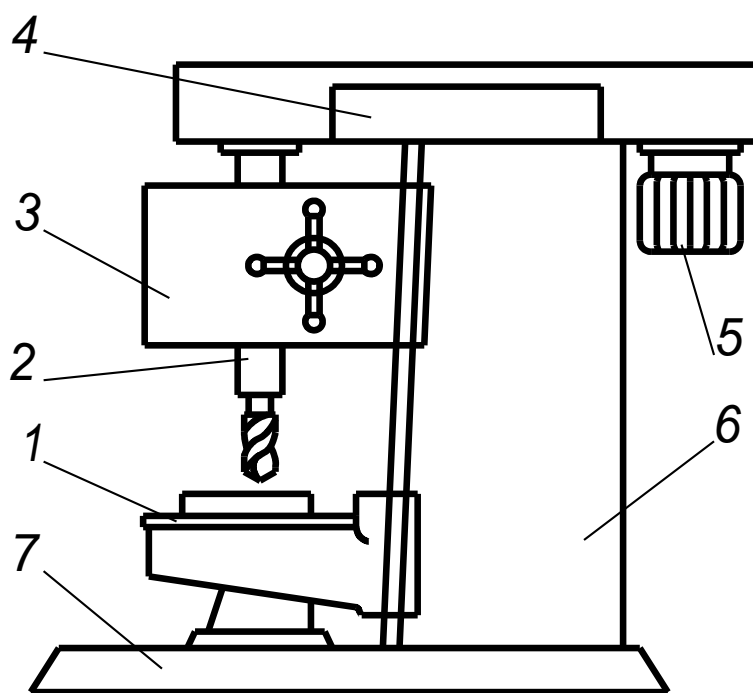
Загальний вигляд вертикально-свердлильного верстата
